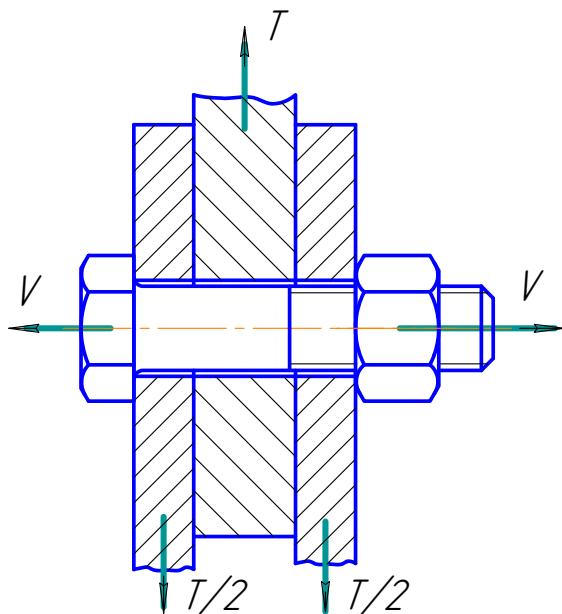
Схема для розрахунку болтового з'єднання, навантаженого поперечною силою
